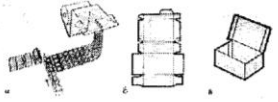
Схема укладання продукції в тару, отриману із плоскоскладеної заготовки: а - схема процесу; б - штампівка заготовки картонної коробки; у - збірка коробки.
